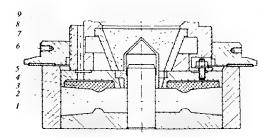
Схема дозирования и укладки формовочной смеси в пресс-форму:
